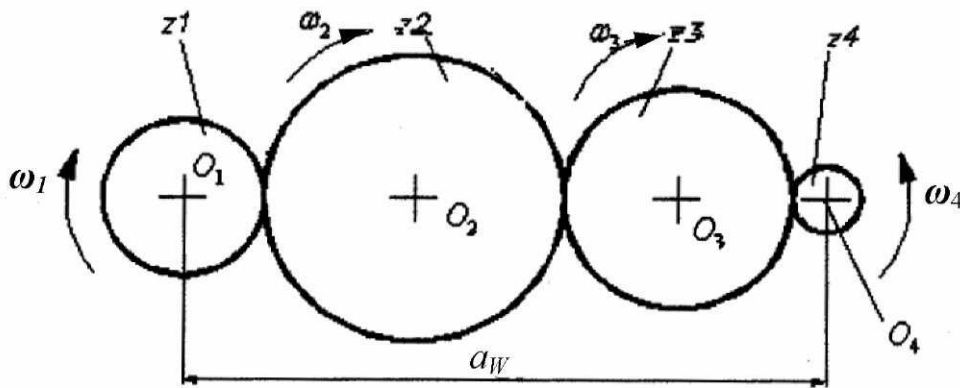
Сложный зубчатый механизм с паразитными колесами
